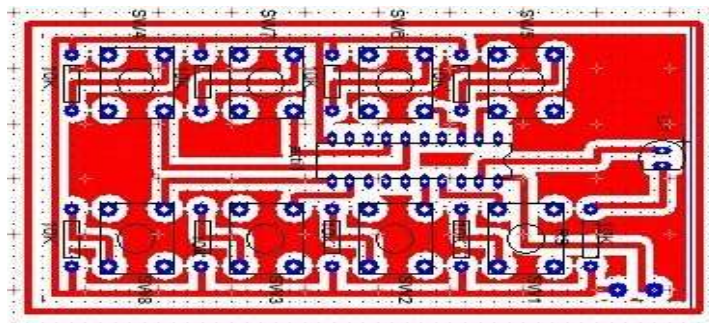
5 Diseño del Circuito Impreso del Control Remoto y sus Componentes.
